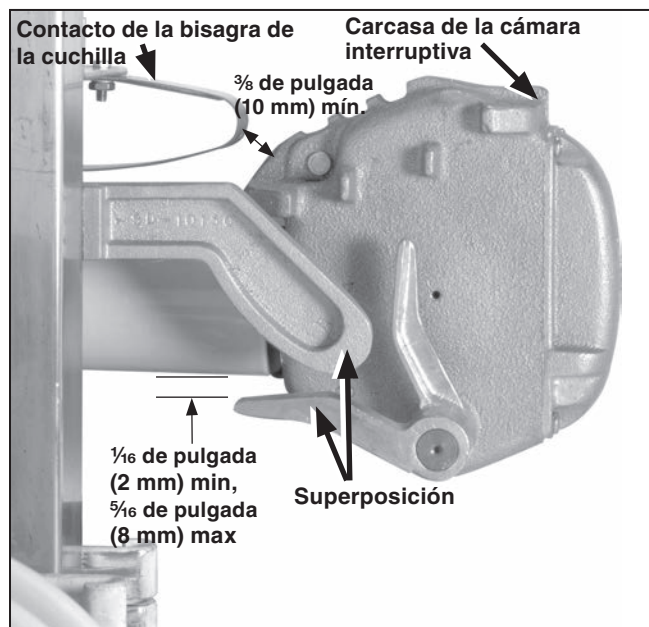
Ensamblaje de la cuchilla en la posición de cierre total.
